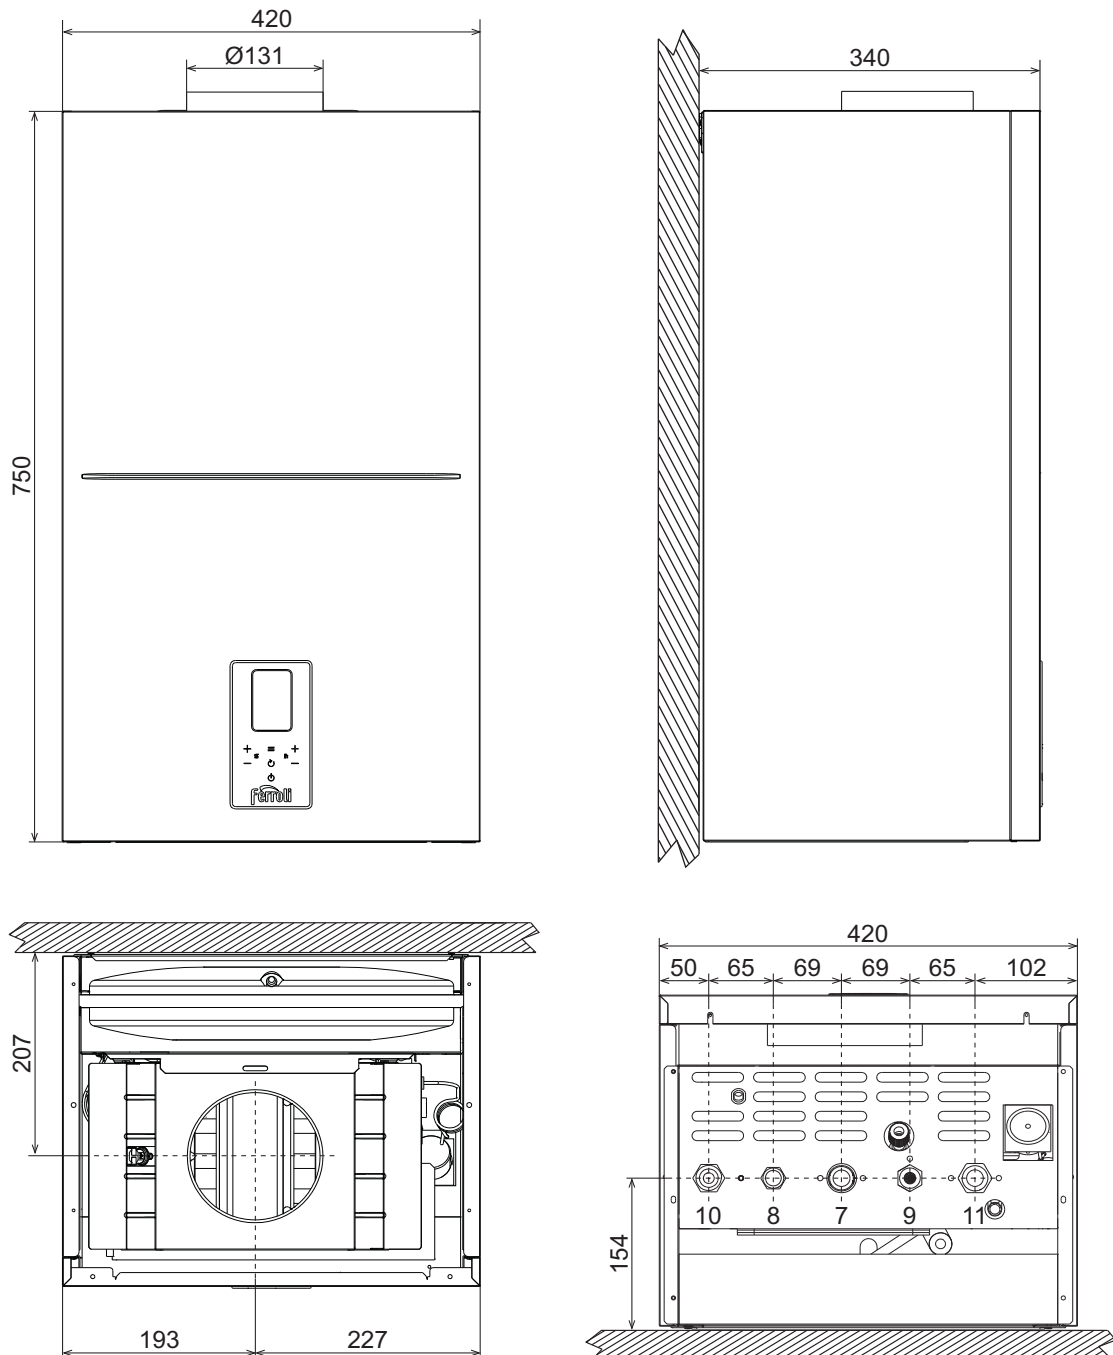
Dimensions et raccords modèle DIVATOP D C24
